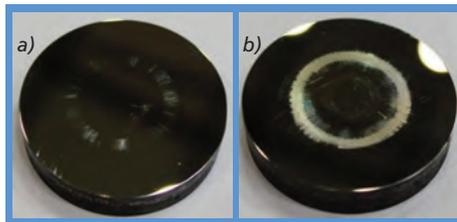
Unbeschichtete Stauchplatten (1.2379)
